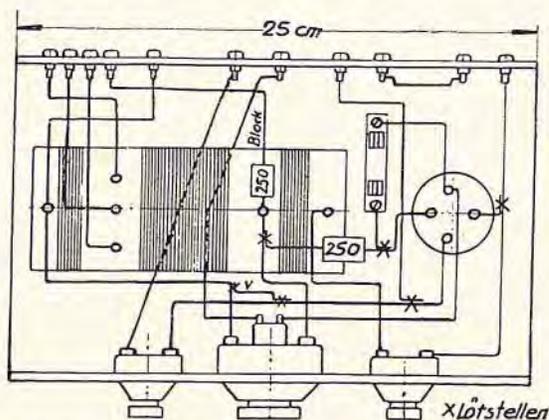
Bodenplatte mit den Bauteilen, geschaltet.
